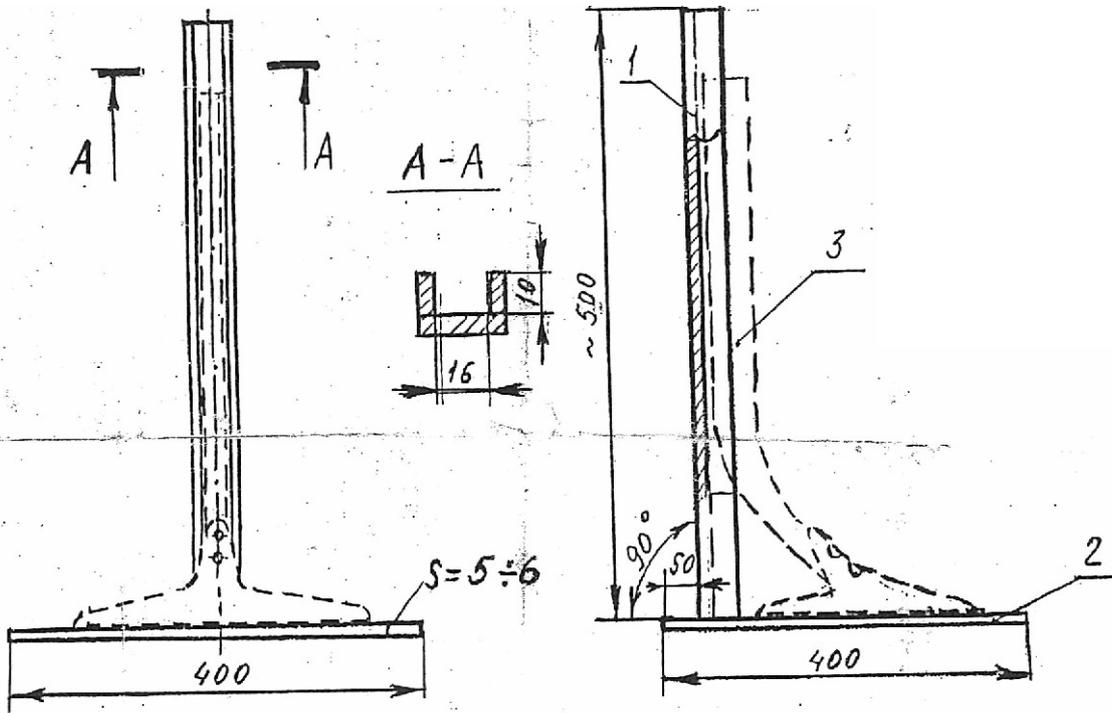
Приспособление для тарировки культиваторных лап со стойкой
